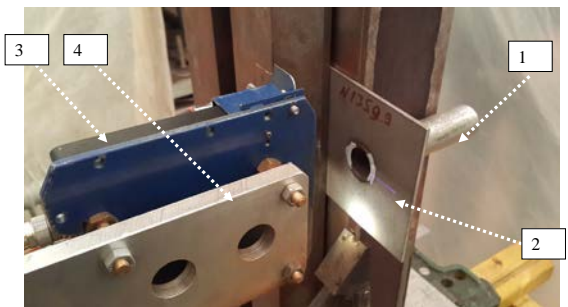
Положення макетного зразка системи пошуку місця зварювання, закріпленого на лабораторному стенді для лазерного зварювання: 1 – зразок, що зварюється; 2 – лінія, згенерована датчиком RiftekRF625; 3 – датчик RiftekRF625; 4 – кронштейни системи кріплення
